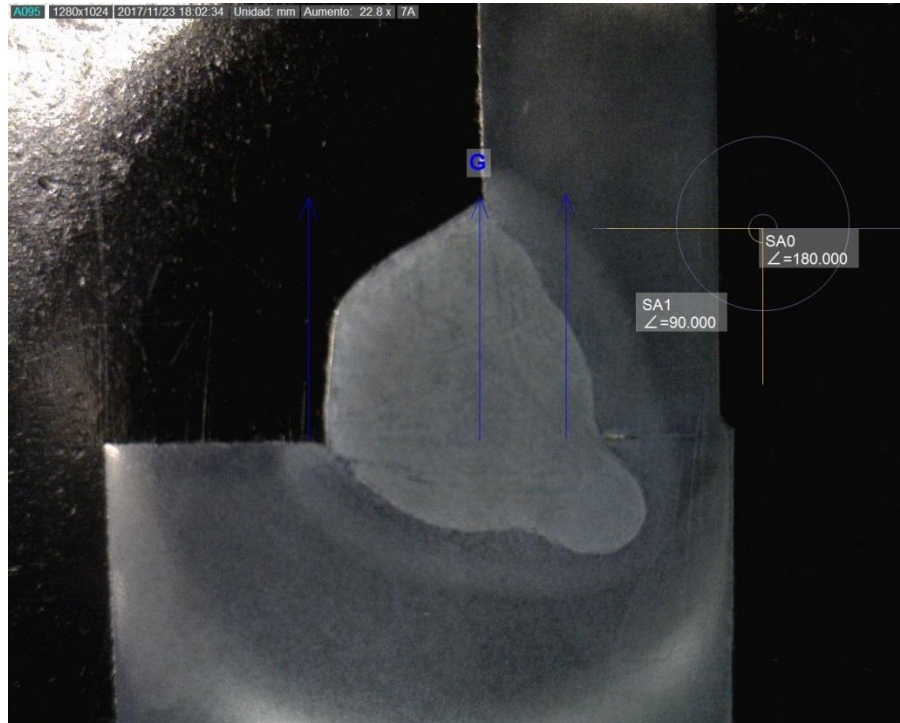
14 Perfil obtenido en cupón de soldadura 7 B.
